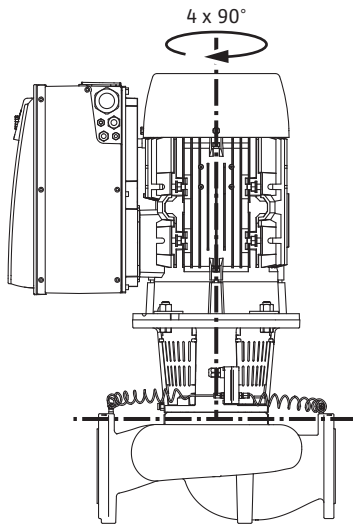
Dikey motor mili ile izin verilen montaj konumları
